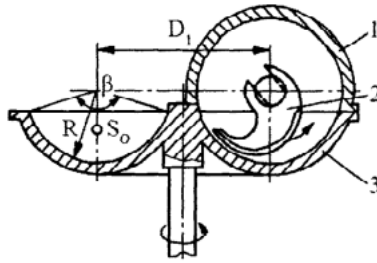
Ріжучий механізм кутера: 1 - кришка; 2 - серповидний ніж; 3 - чаша
